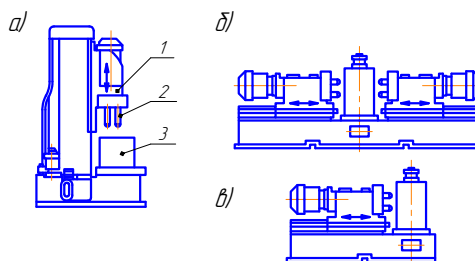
Типовые компоновки силовых приводов агрегатных станков для обработки системы отверстий: а, б, в: 1 — многшпindelная головка; 2 — инструмент; 3 — заготовка.
